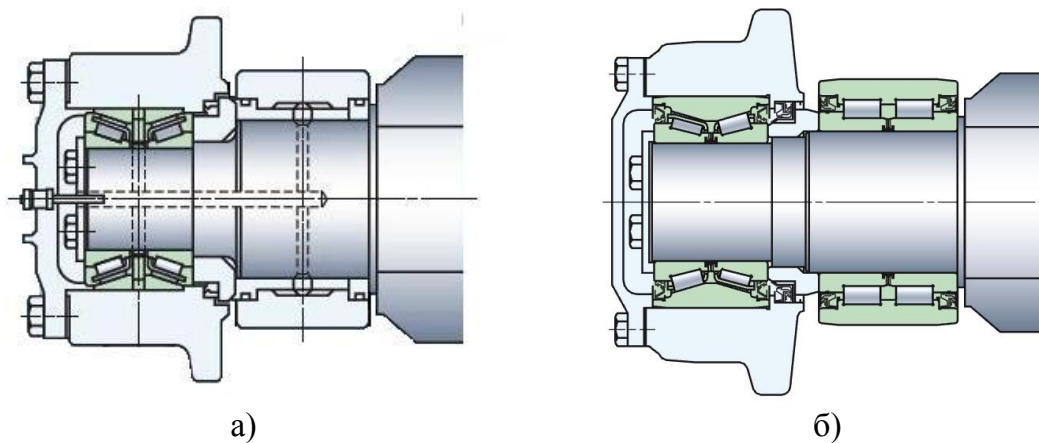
Роликові вузли для візків з підшипниками фірми «NSK»: а) – традиційна конструкція; б) – нова конструкція
